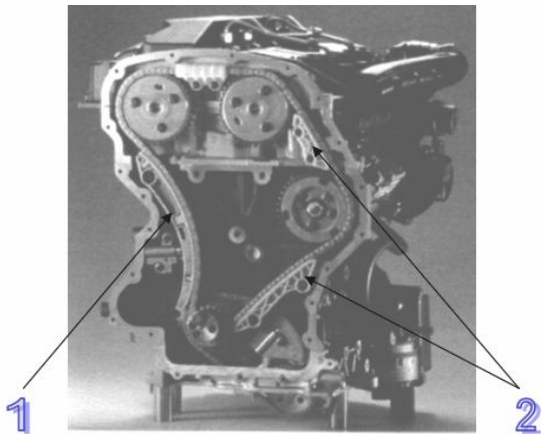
Ланцюгова передача приводу газорозподільного механізму дизельного двигуна
